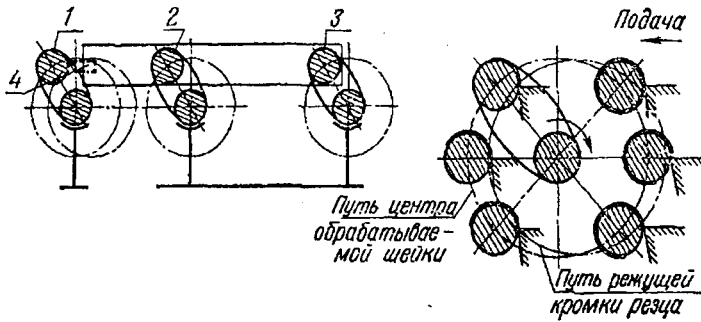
Схема одночасного обточування всіх шатунних шийок колінчастого валу: 1 – оброблювана шийка; 2 і 3 – кривошипи супорта; 4 – різець.
